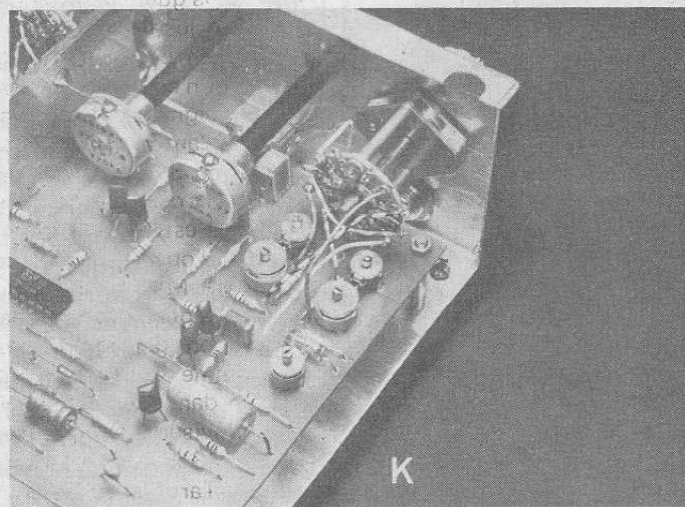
Photo K. - Gros plan sur le câblage d'un atténuateur d'entrée. Remarquer aussi le fil de masse des boîtiers de potentiomètres.
